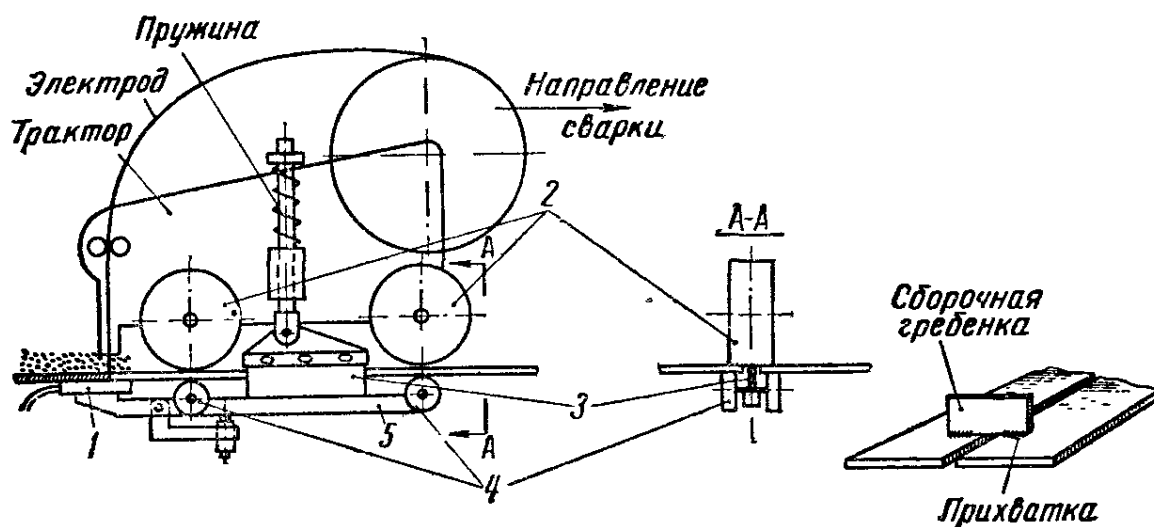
Сварка листов в стык с зазором на медном скользящем башмаке трактором ТС-32
